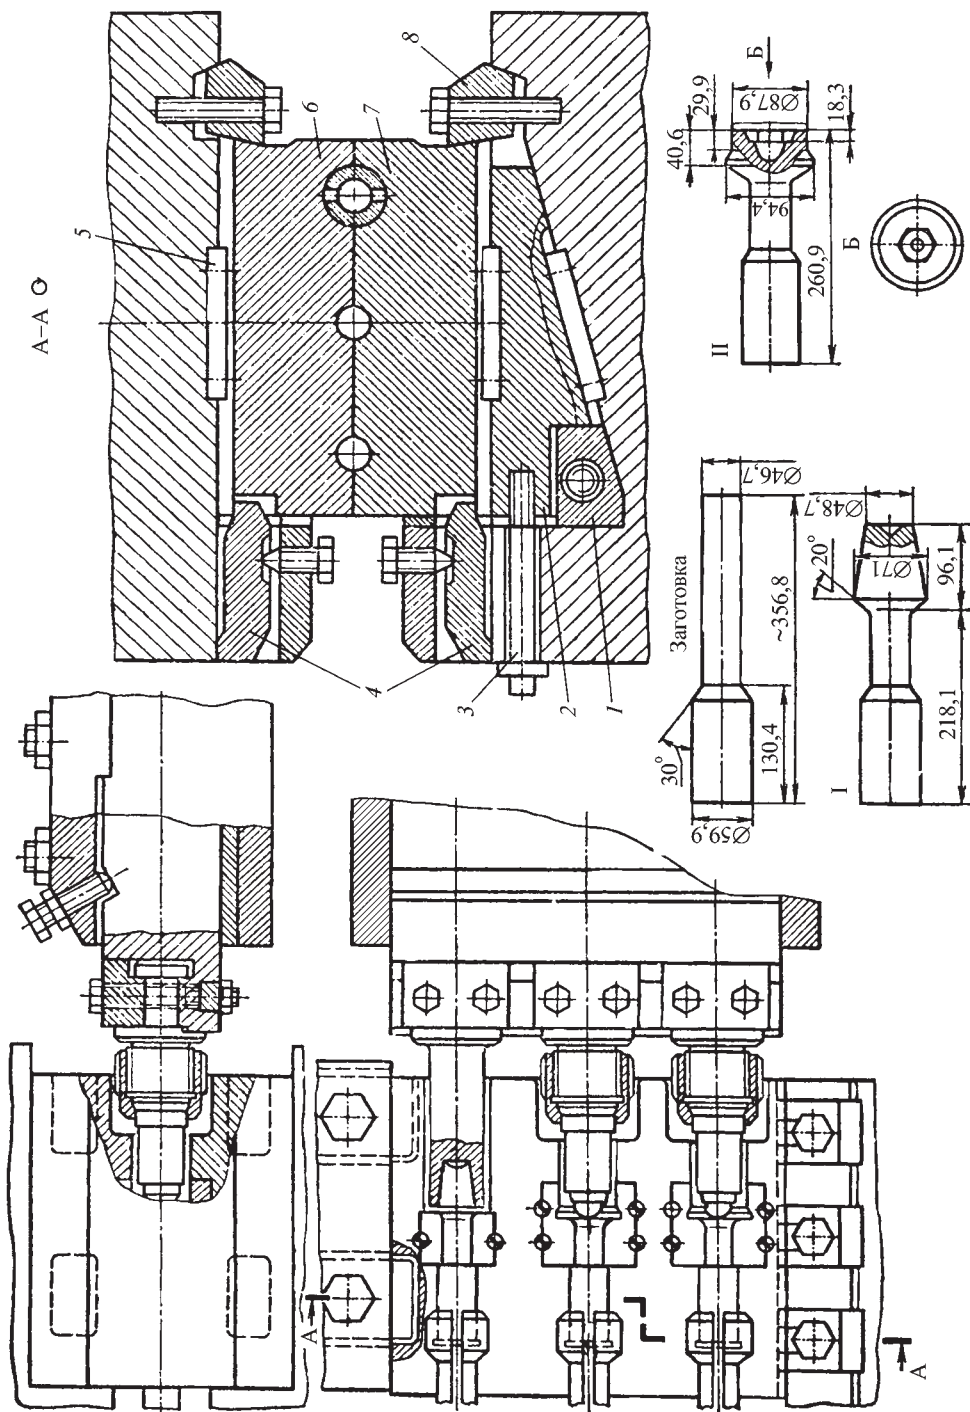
Штампы с горизонтальным разъемом матрицы для изготовления поковки шлицевого конца вала
